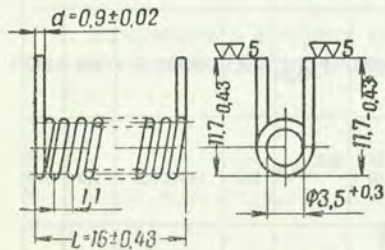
Данные для изготовления винтовых цилиндрических пружин
